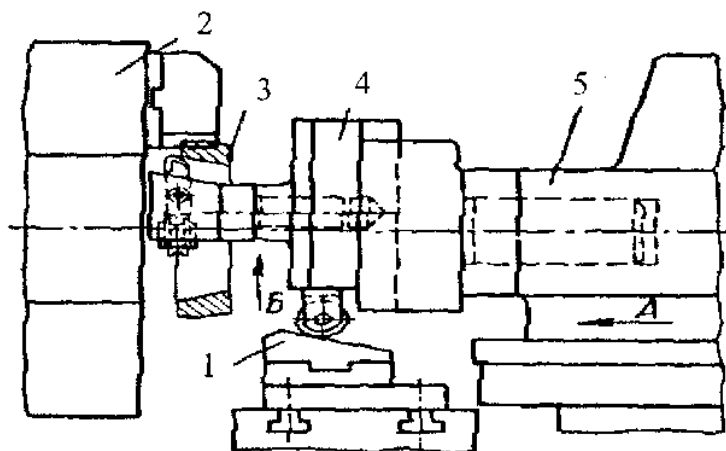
Схема копіювального пристрою до револьверного верстата
